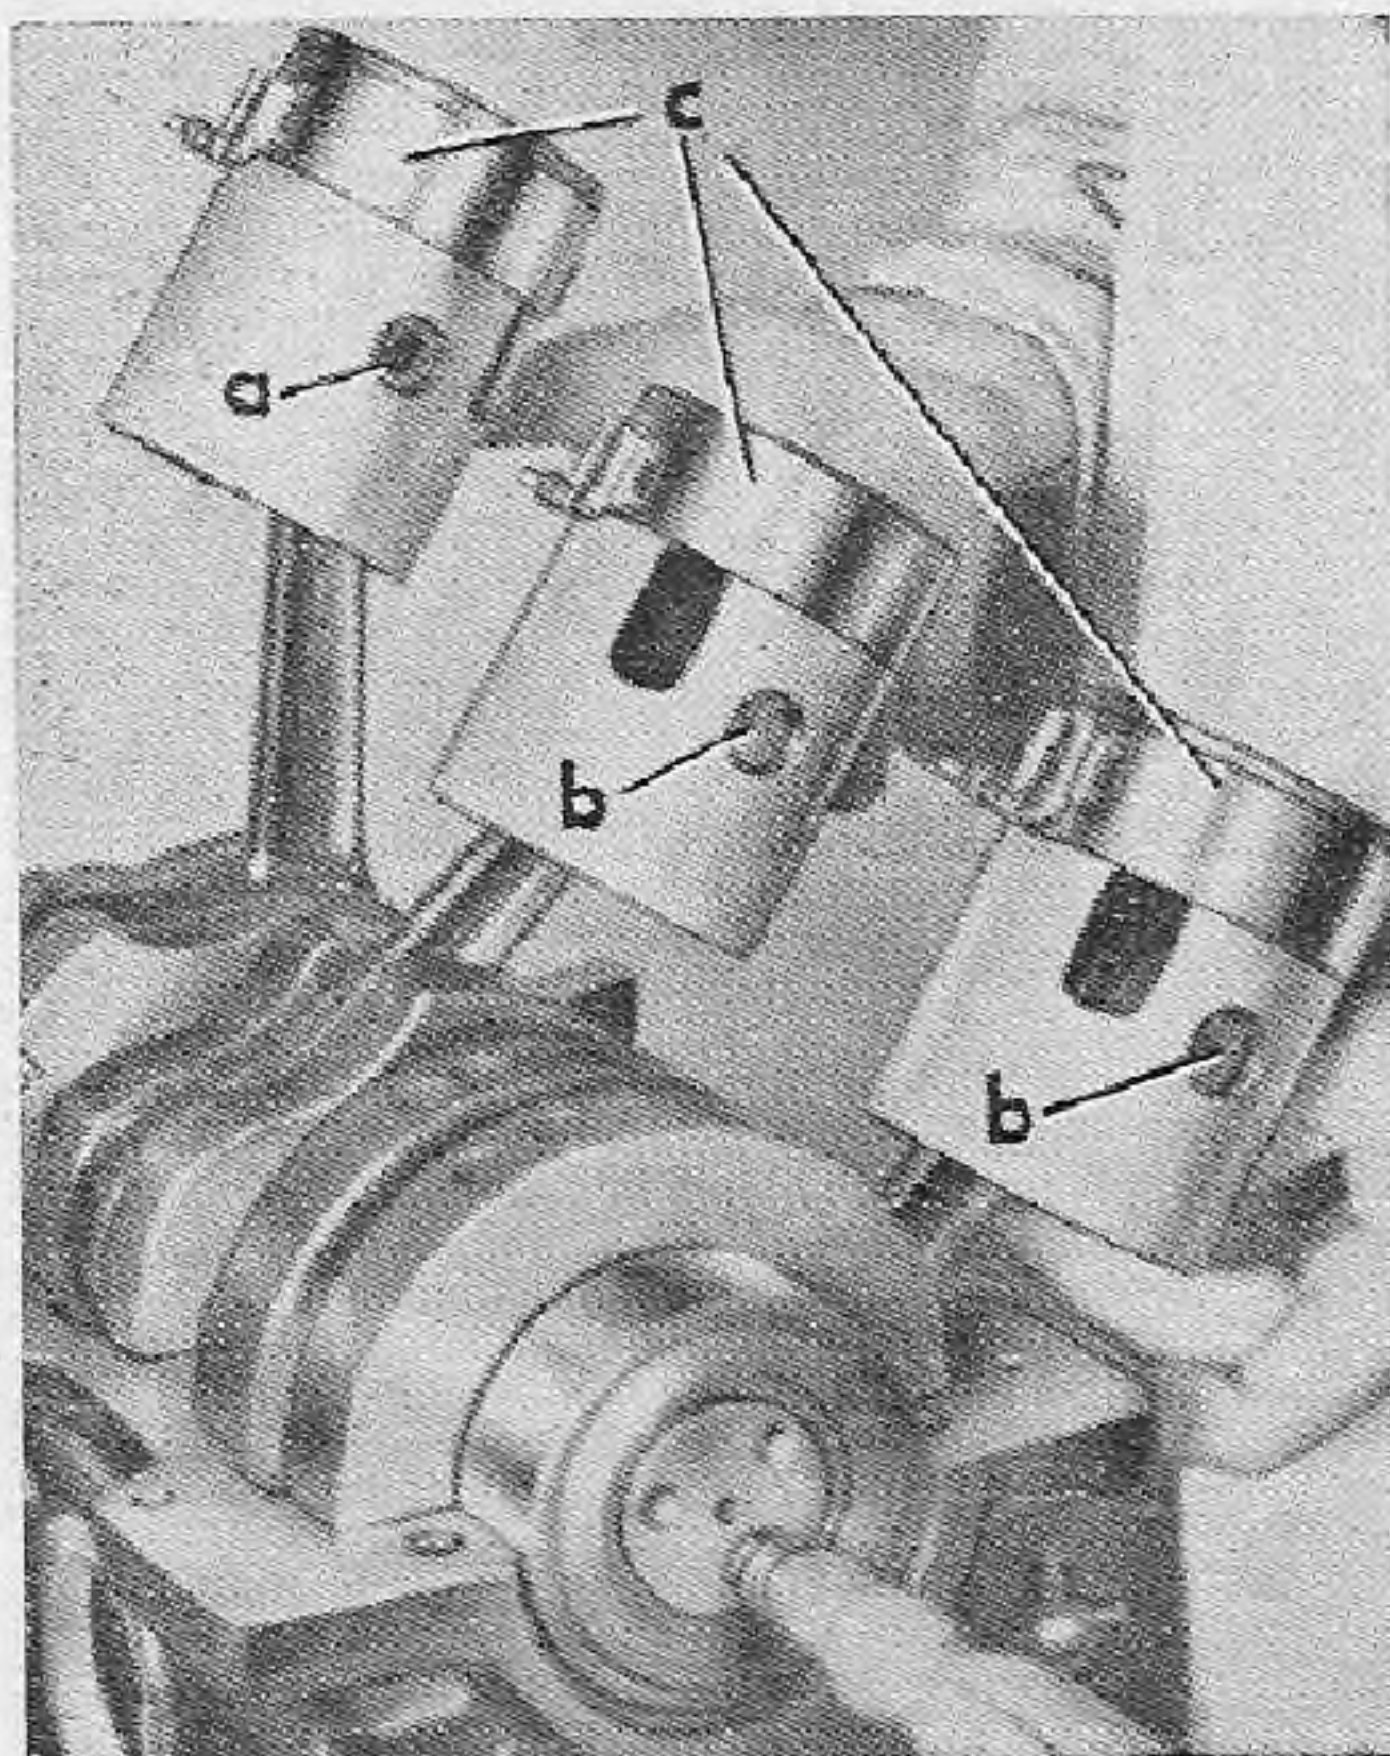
Posición correcta de montaje de los pistones y pernos de pistón.
